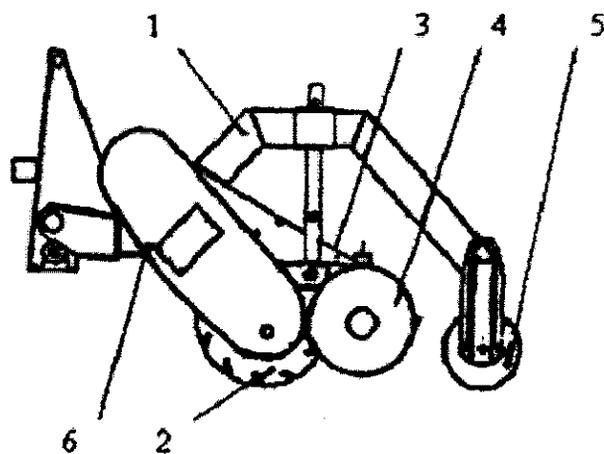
Конструктивная схема экспериментальной установки: 1-рама; 2-фрезбарабан; 3-кожух ротора; 4-колесо опорное фрезбарабана; 5- прикатывающий каток; 6-привод фрезбарабана
